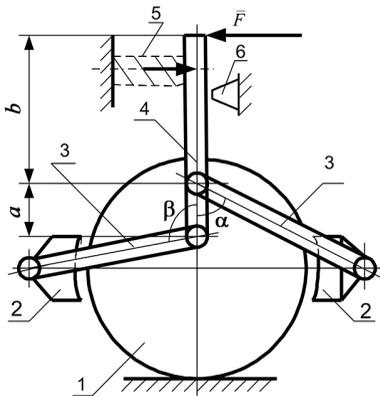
Схема механического привода с плавающим рычагом к тормозным колодкам катящегося колеса:
